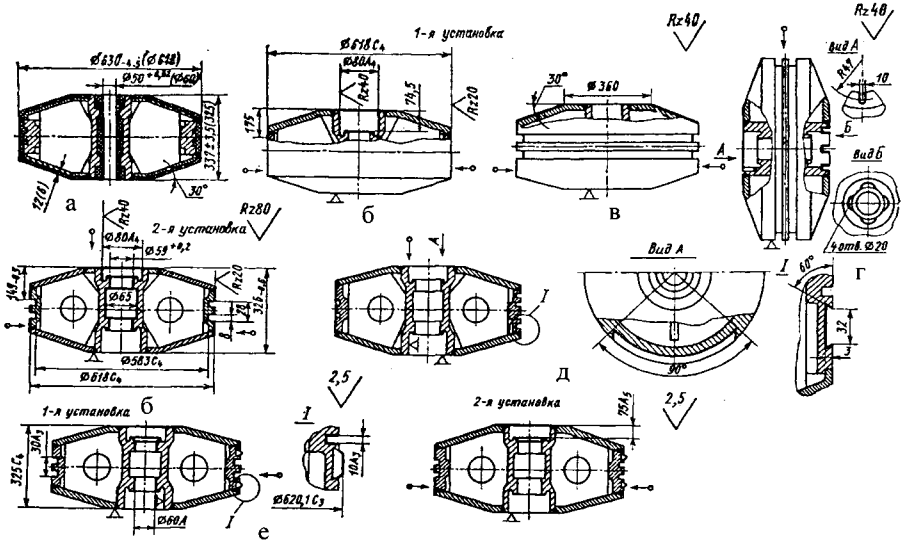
Технологічна схема механічної обробки поршня $\varnothing 620$ мм опозитного компресора 4М10-100/8.
